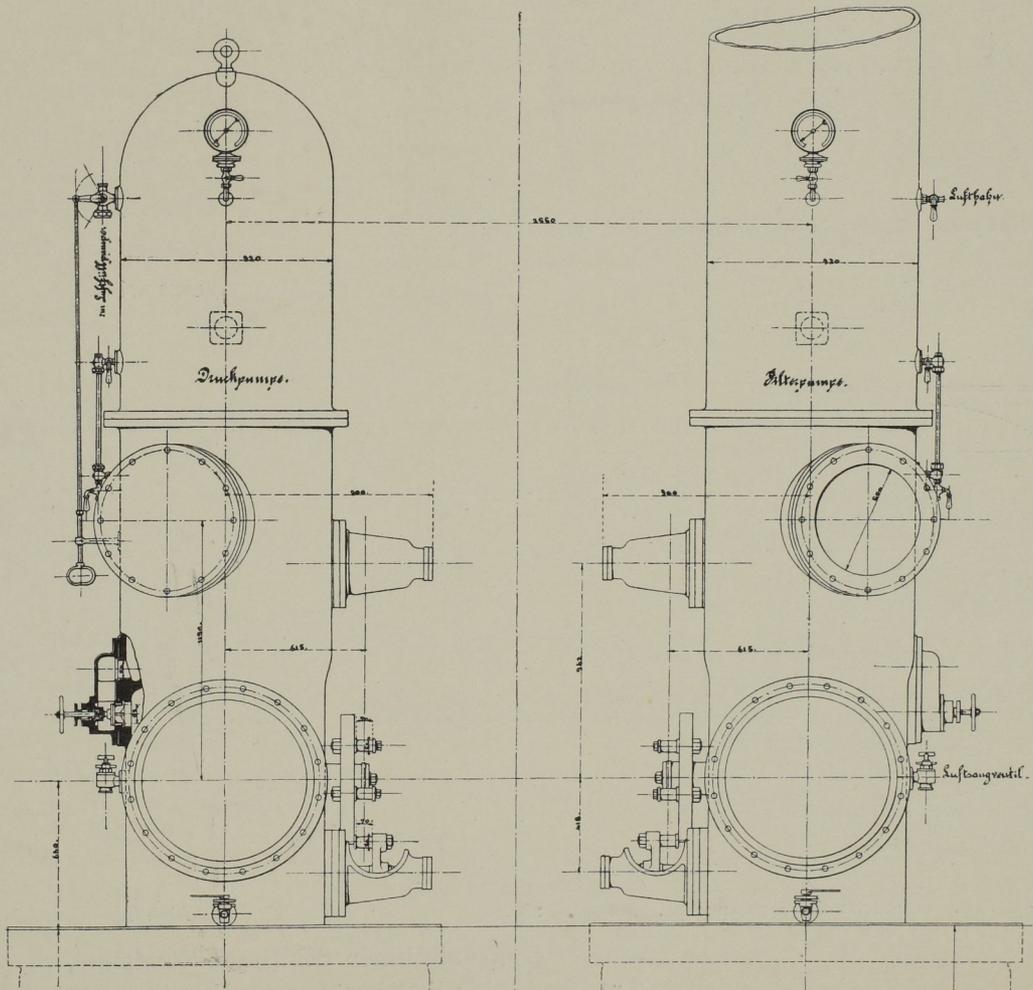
Stirnansicht der Druck- und Filterpumpe. Masst. 1:30.
